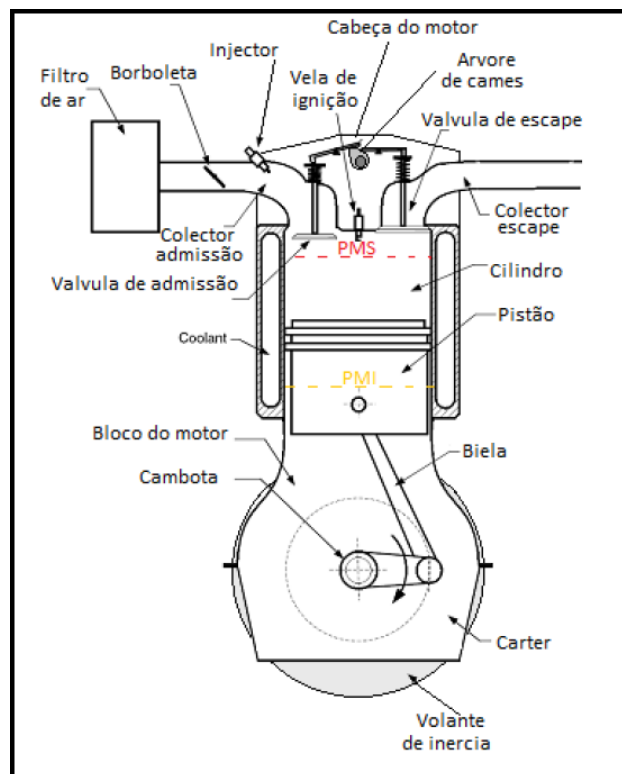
Esquema de um motor de combustão interna monocilíndrico.
